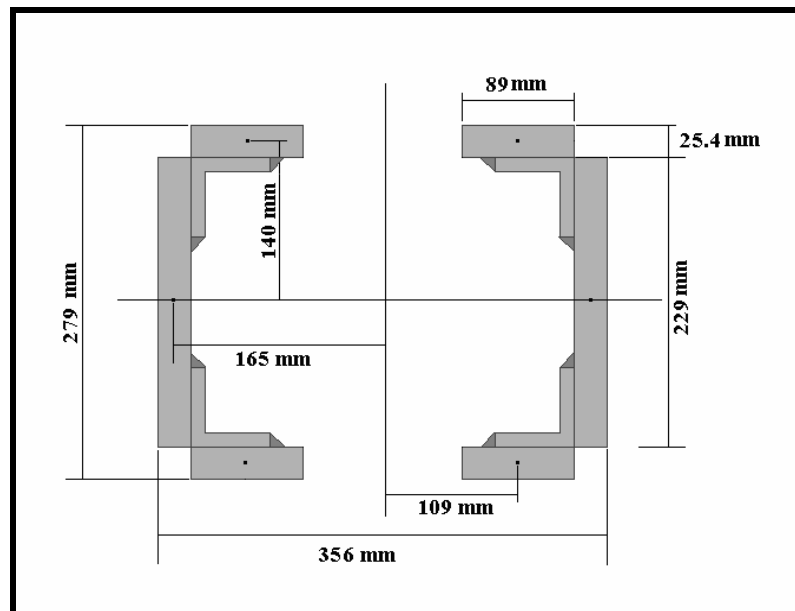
Se muestra la forma y las medidas de la sección transversal de una de las columnas del bastidor de salida
